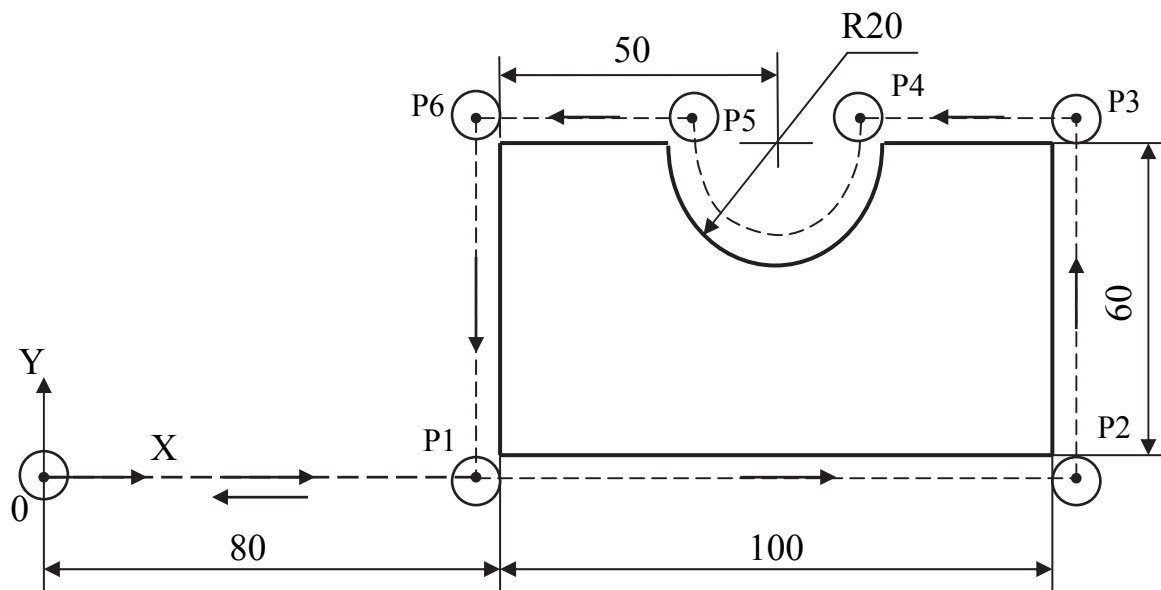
Схема изготовления детали на фрезерном станке с ЧПУ
